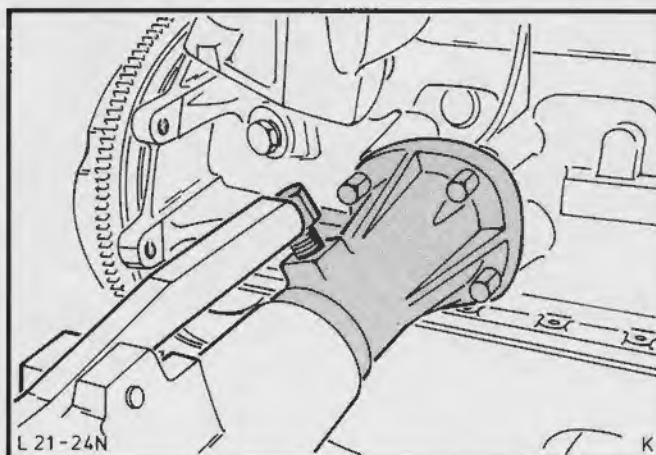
Spænd motoren op i motorstativet med holdearmen 21-031
